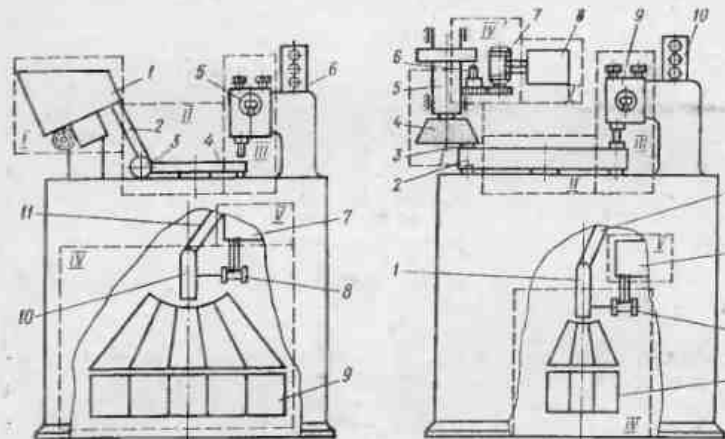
Конструктивная схема контрольной системы для пассивного контроля; 1 — загрузочный бункер; 2 — первичный лоток; 3 — отсекающий; 4 — транспортирующий механизм; 5 — первичный преобразователь (датчик); 6 — светофорное табло; 7 — запоминающе-усилительный блок; 8 — блок перевода рукава; 9 — отсеки; 10 — рассортировывающий рукав; 11 — вторичный лоток. Основные органы контрольных систем: I — загрузочный; II — транспортирующий; III — измерительный; IV — исполнительный; V — запоминающе-усилительный
